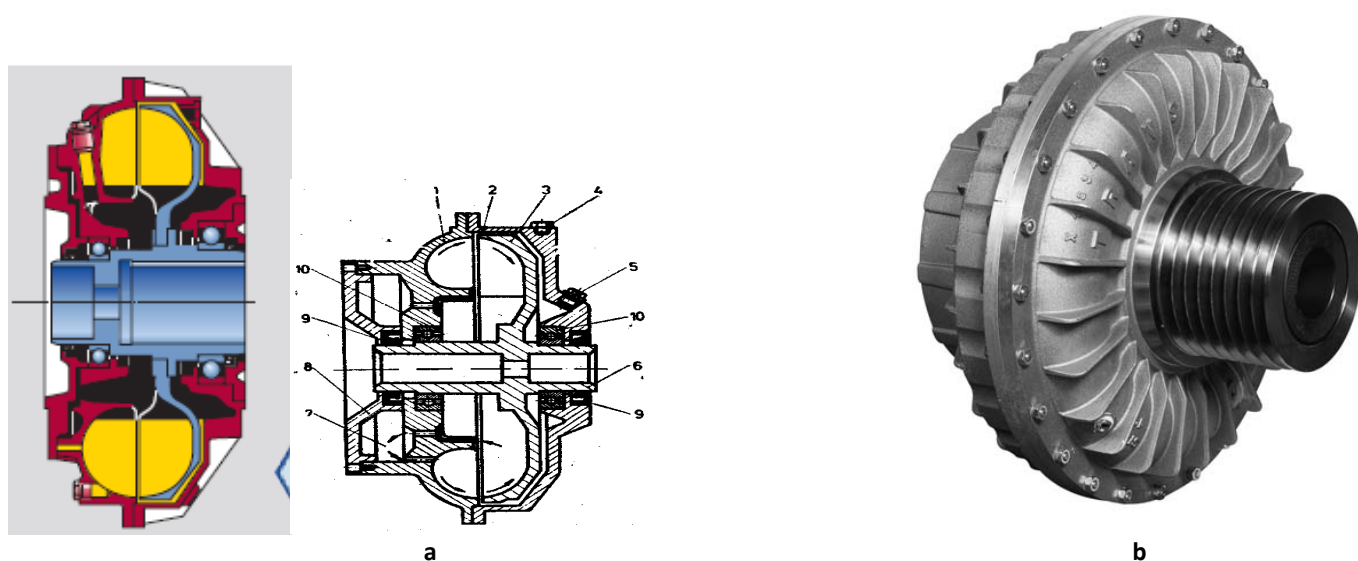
Turboambreaaj industrial: a) componenta: 1- rotor pompă; 2-carcasă; 3-rotor turbină; 4-dop fuzibil; 5- dop umplere; 6- arbore secundar; 7- rezervor; 8-capac; 9- etanșare; 10-rulment. b) fotografia.
